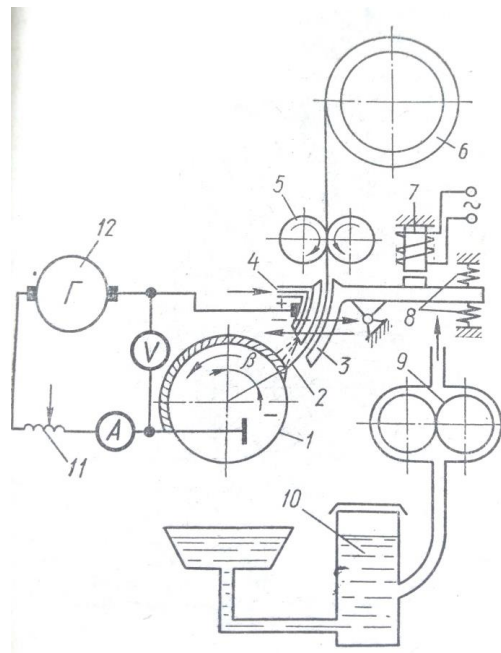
Принципова схема установки для автоматизованого електровібраційного наплавлення шару металу на деталь 1 - деталь, яку наплавляють; 2 - електрод; 3 - вібраційний мундштук; 4 - канал для подачі рідини; 5 - ролик подавального механізму; 6 - касета для дроту; 7 - вібратор; 8 -
